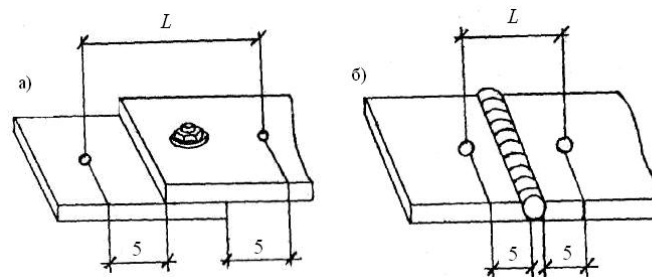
Места измерения электрического сопротивления разборных и неразборных контактных соединений: (а) шин болтами; (б) шин сваркой
